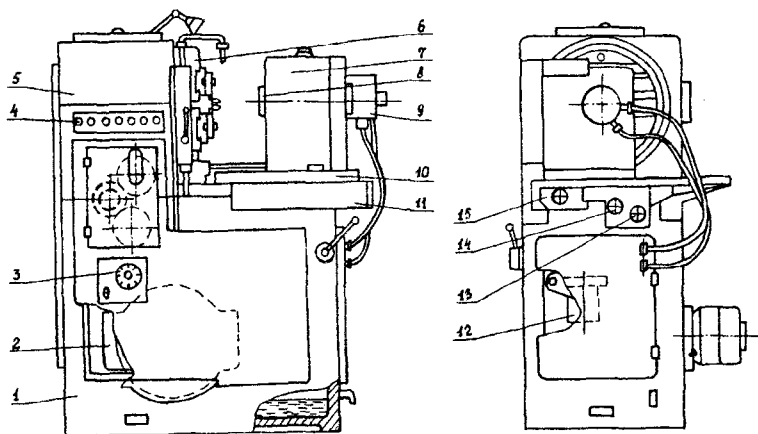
Общий вид зубострогательного станка модели 51123Б
